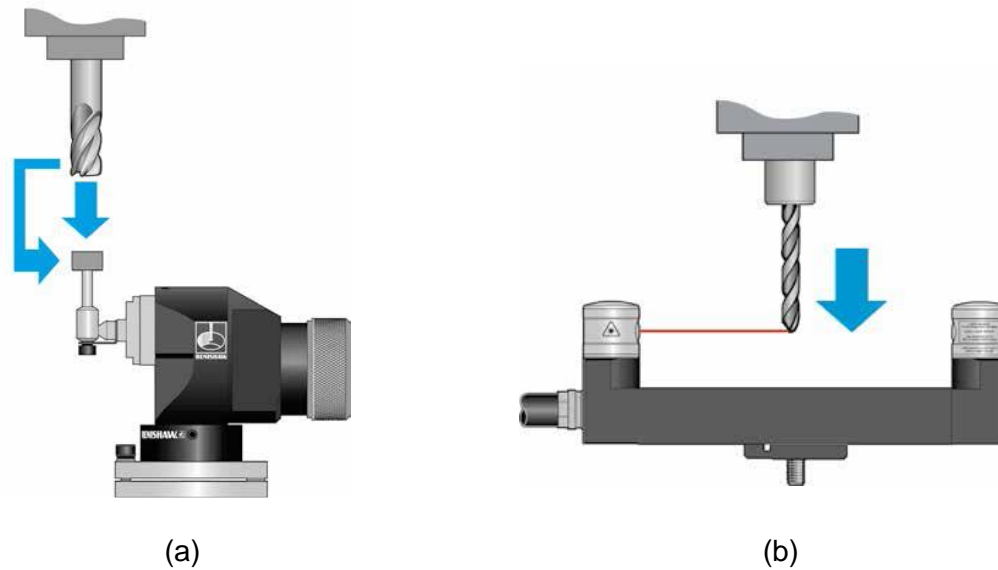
Sistema de medição de ferramentas: (a) por contacto; (b) sem contacto, laser (Renishaw, Probing Systems for CNC Machine Tools, 2014)
